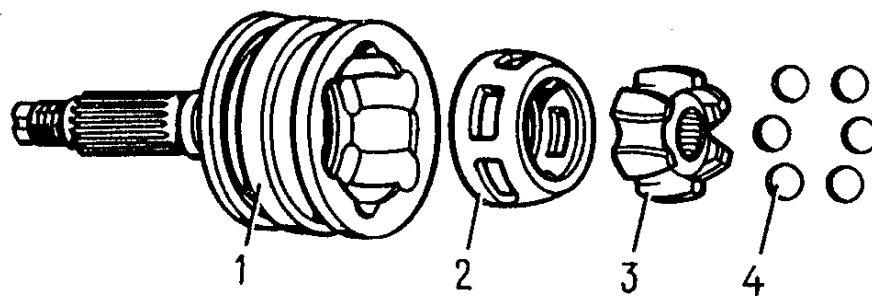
Piezas de la junta exterior de accionamiento de las ruedas delanteras
